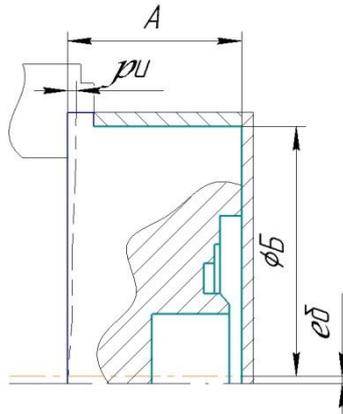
Схема подрезки торца и обточки заготовки на операции 020
